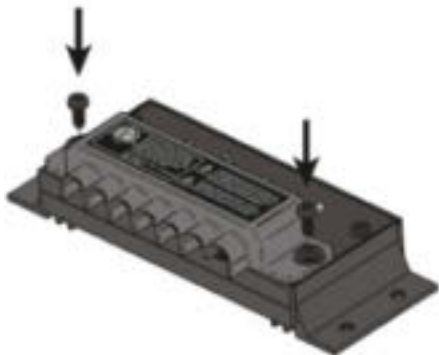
Befestigen der Klemmenblende mit 2 Schrauben.
